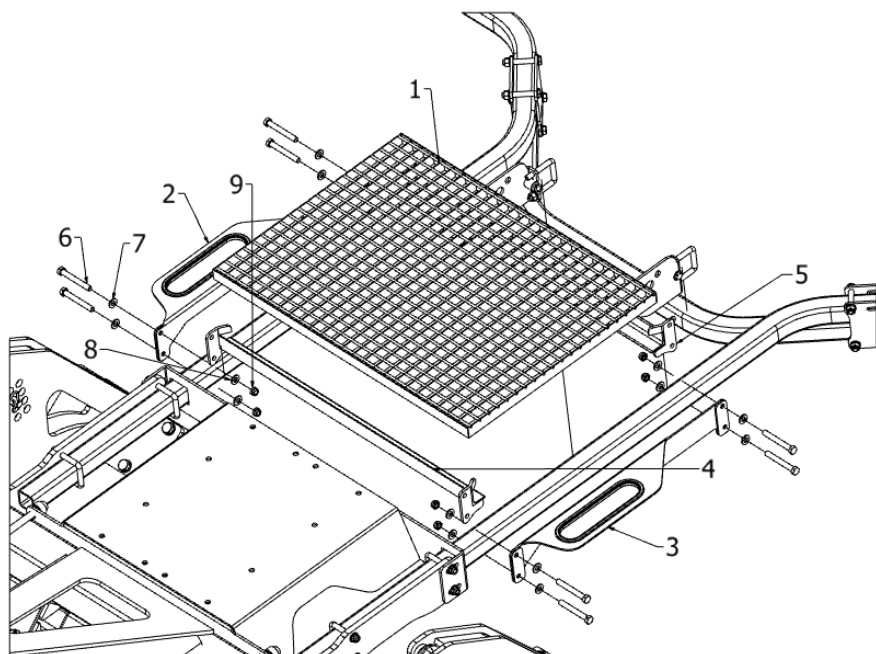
Befestigung der Sämaschinenplattform am Maschinenrahmen.
